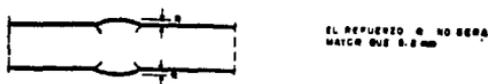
b) Perfil aceptable en soldadura de ranura a tope.
